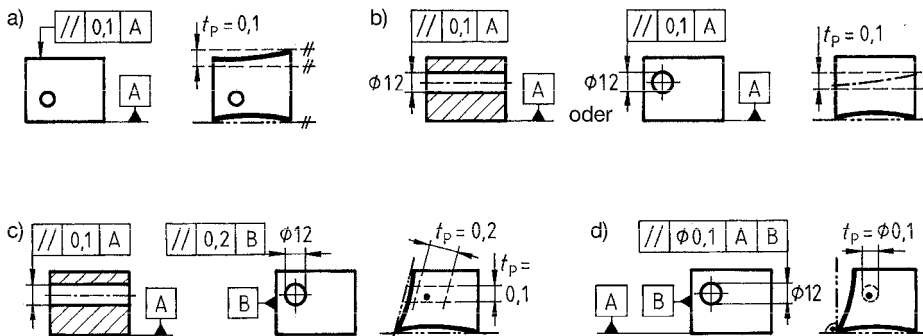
Parallelitätstolerierung mit ebenen Bezugselementen. a) Planflächen toleriert, b) Bohrung mit 1 Bezug, c) Bohrung mit 2 Bezügen, d) Bohrung mit Bezugssystem
